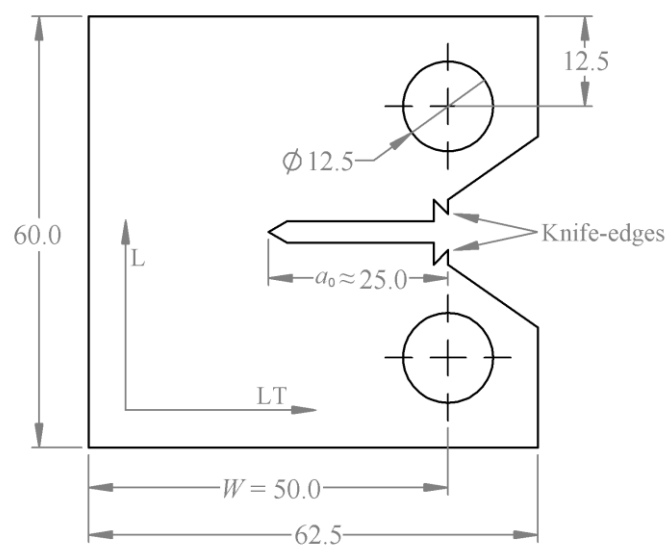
Corpo de prova C(T) com  $W = 50$  mm. Dimensões em milímetros
